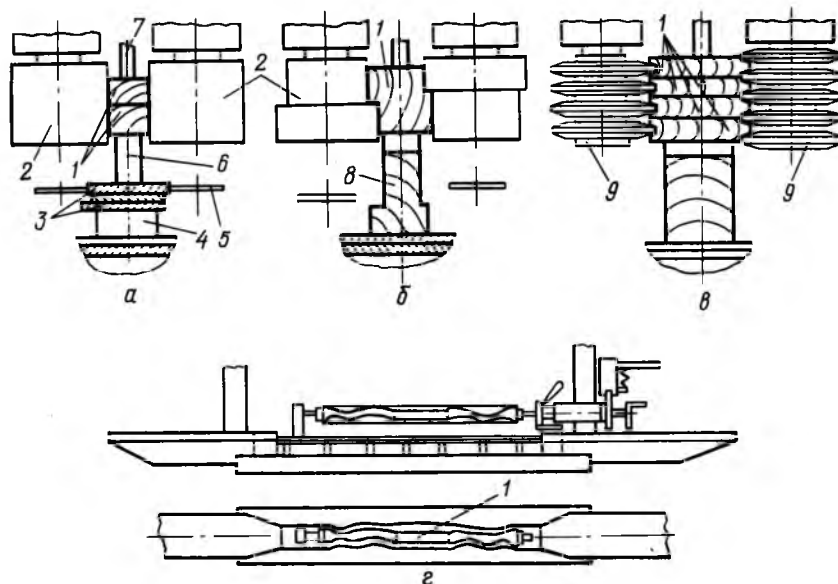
Схемы обработки деталей на полуавтомате ФКД5:
